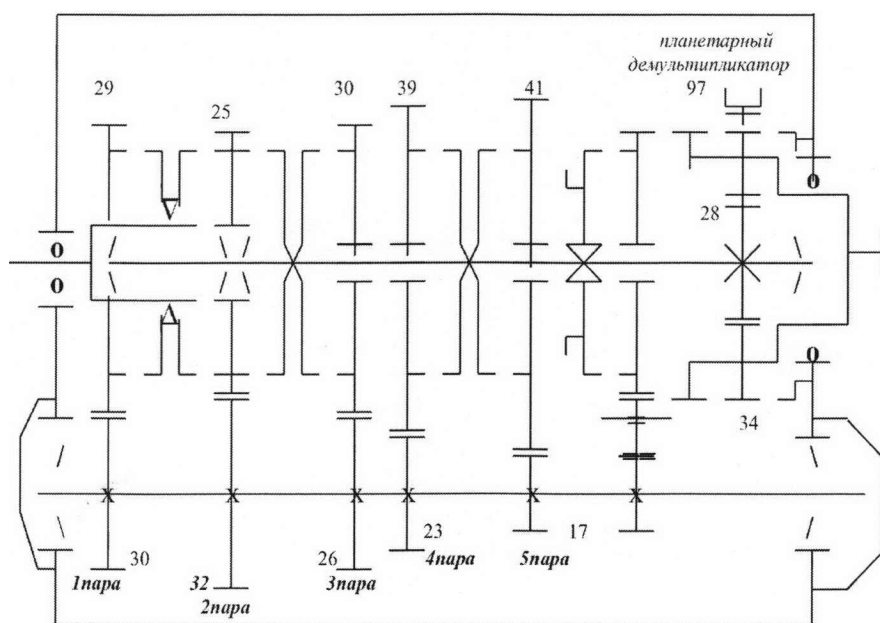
Кинематическая схема 16 ступенчатой коробки передач ТМ16-2000
